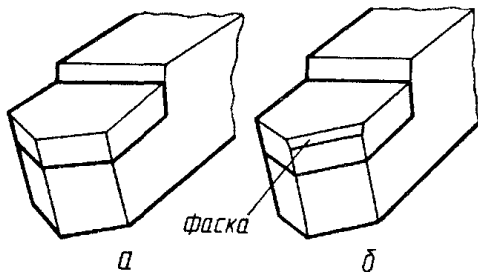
Форми передньої поверхні твердосплавного різця:
